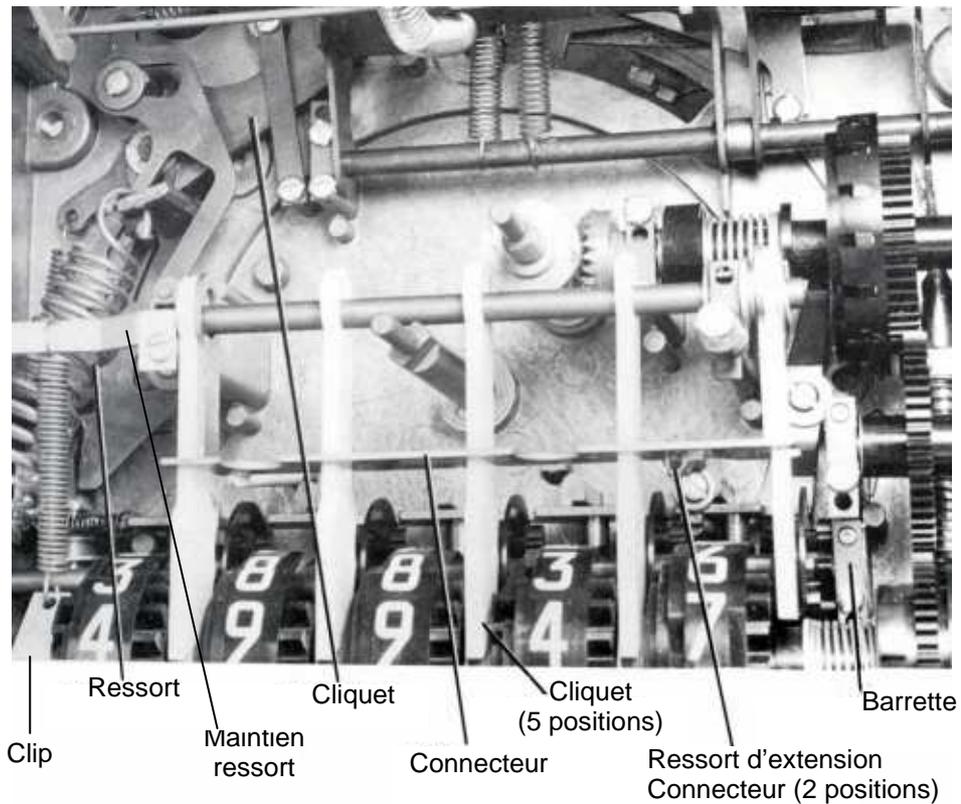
Identification des pièces du prédéterminateur (Roues enlevées)
